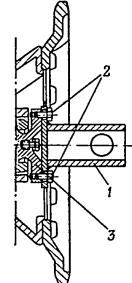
Ключ для вывешивания пробки ведущего колеса: 1 — ключ; 2 — стопорные болты; 3 — пробка.
